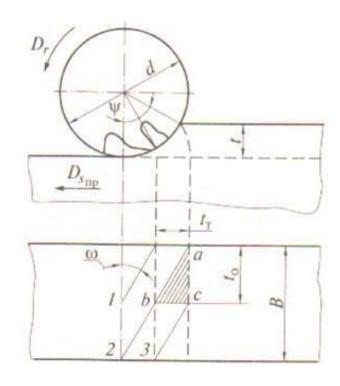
Схема расположения зубьев при равномерном фрезеровании 1, 2. 3 — развертка на плоскость винтовых зубьев фрезы; t — глубина резания; Ψ - угол, охватывающий обрабатываемую поверхность; ω — угол наклона зуба; abc — треугольник, катетами которого являются шаги зубьев; остальные обозначения см. на рис. 2
